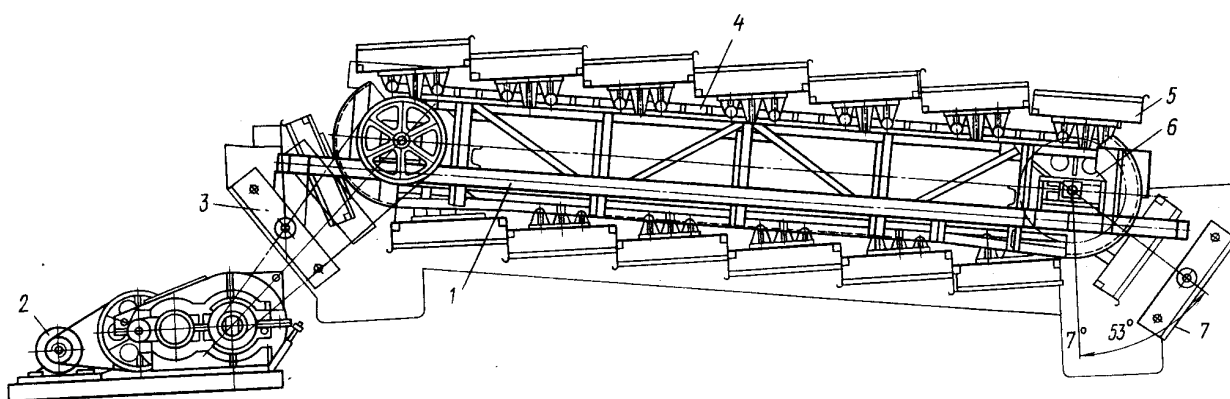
Металлический подвижный шлюз (ШМС):
